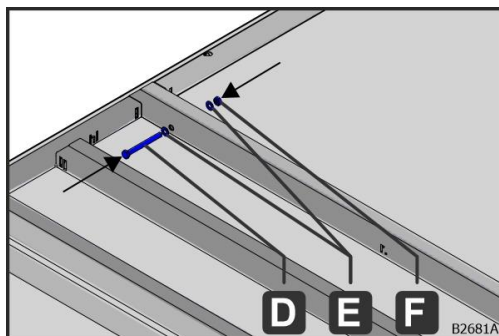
Detaliu îmbinare cu șuruburi cadru suplimentar
